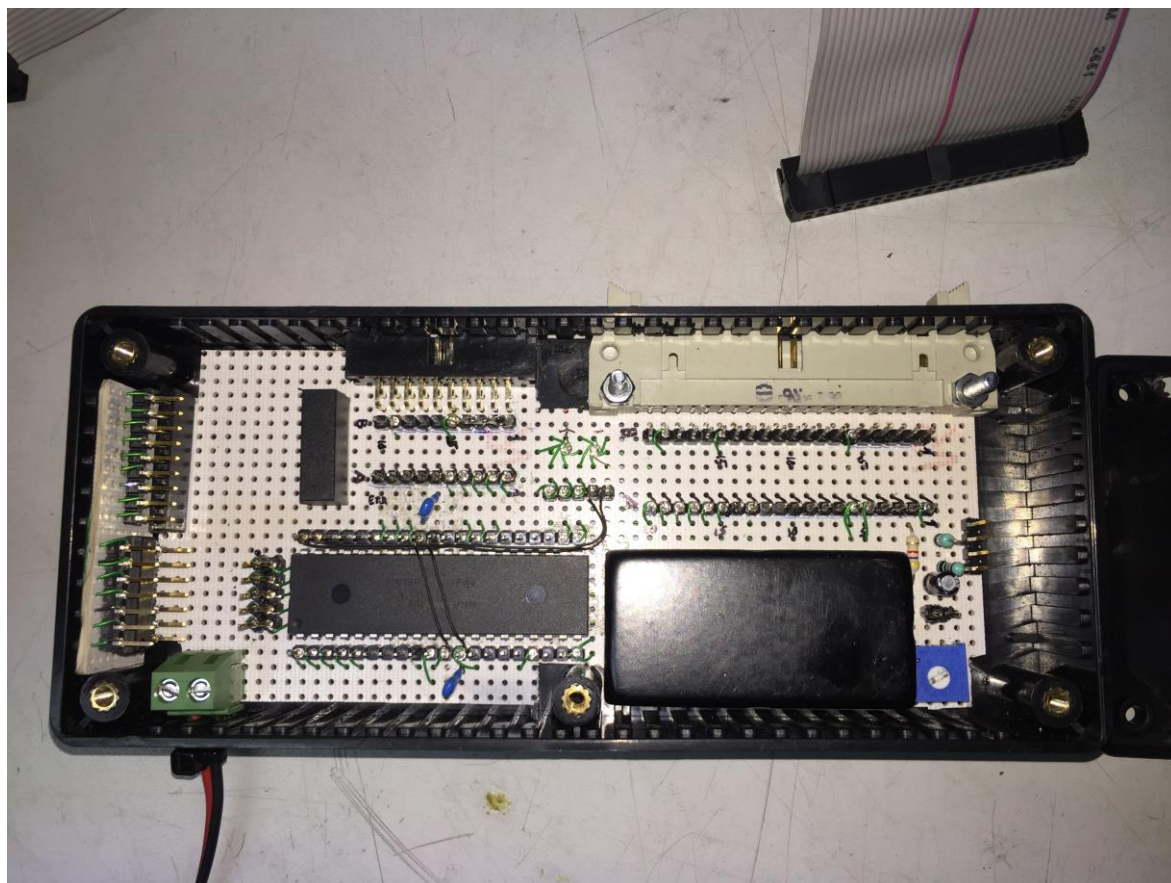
PCB com o circuito de alimentações e microcontrolador já montado
